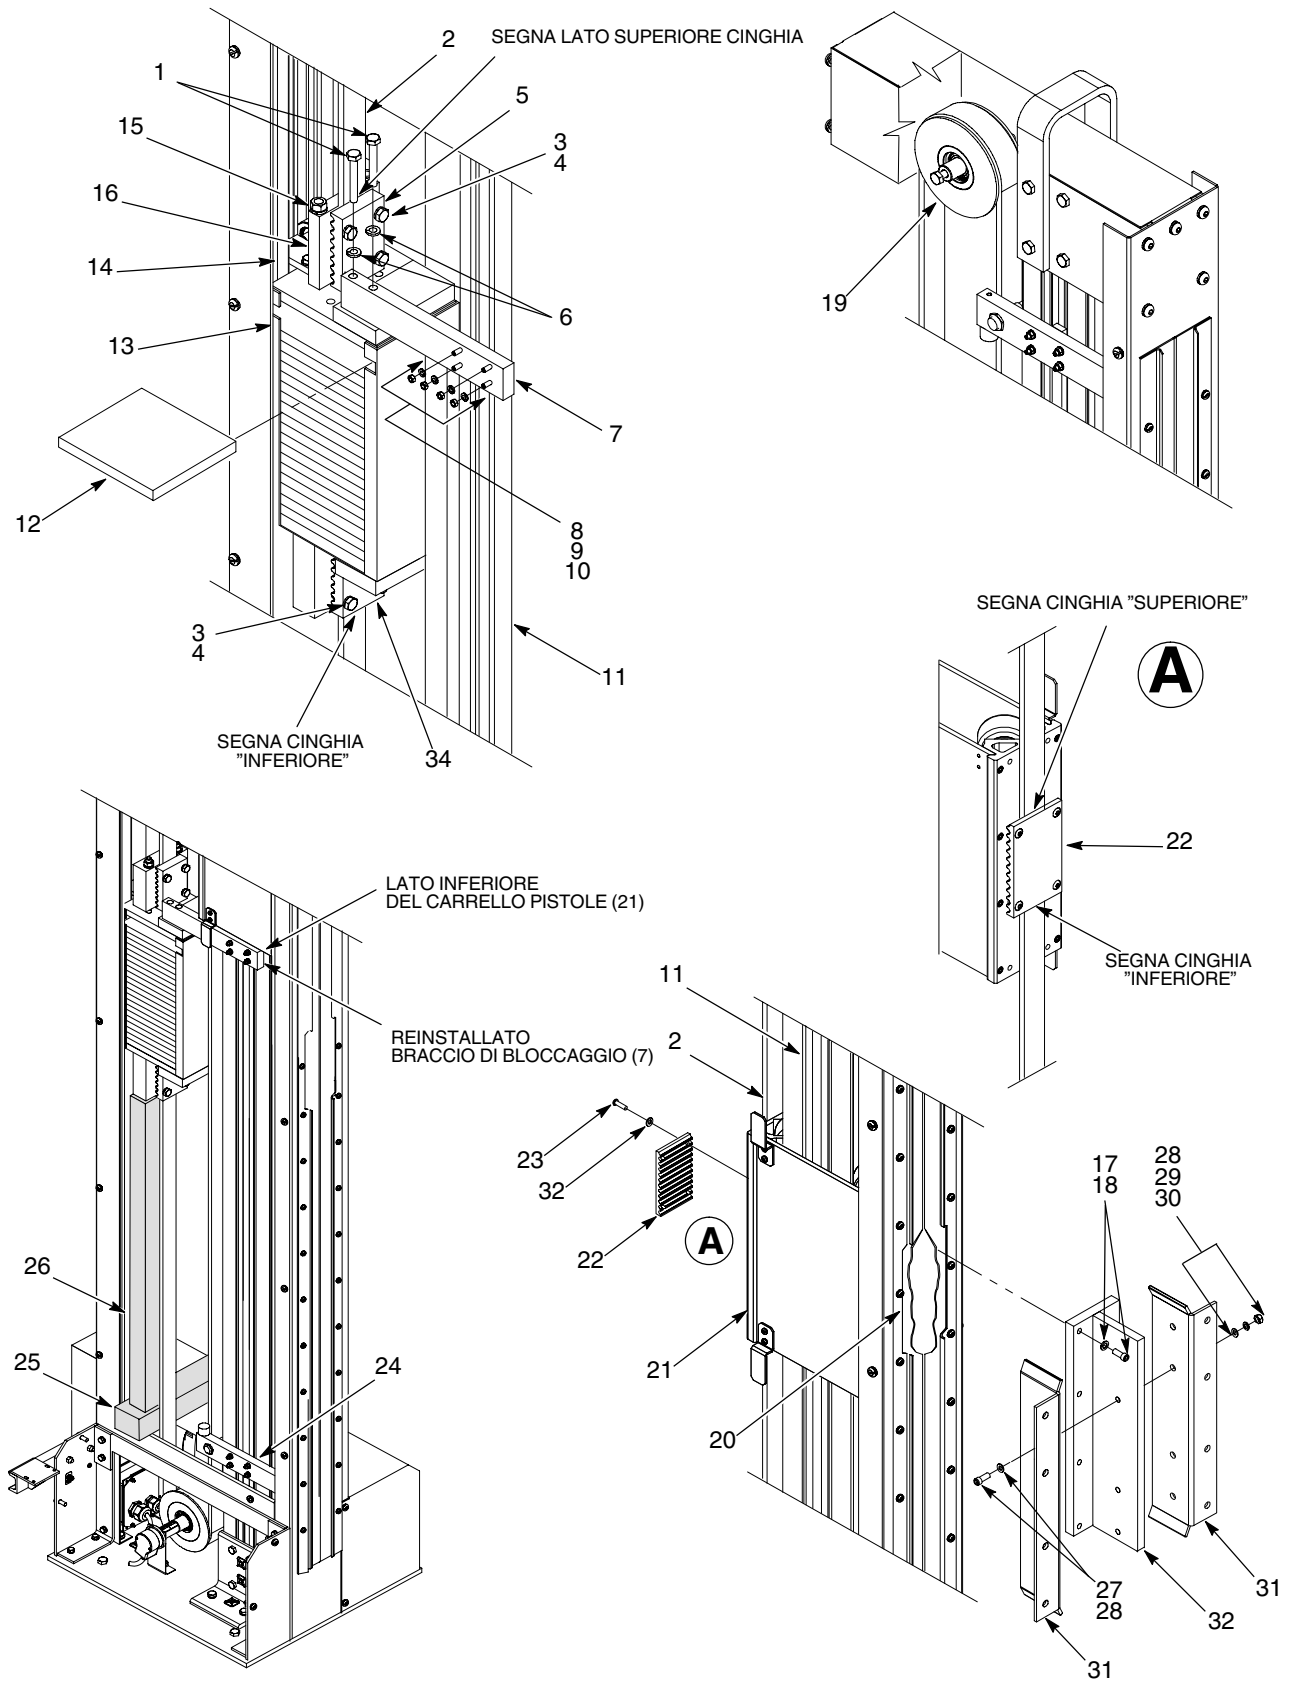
Installazione del dispositivo di montaggio del carrello pistole
